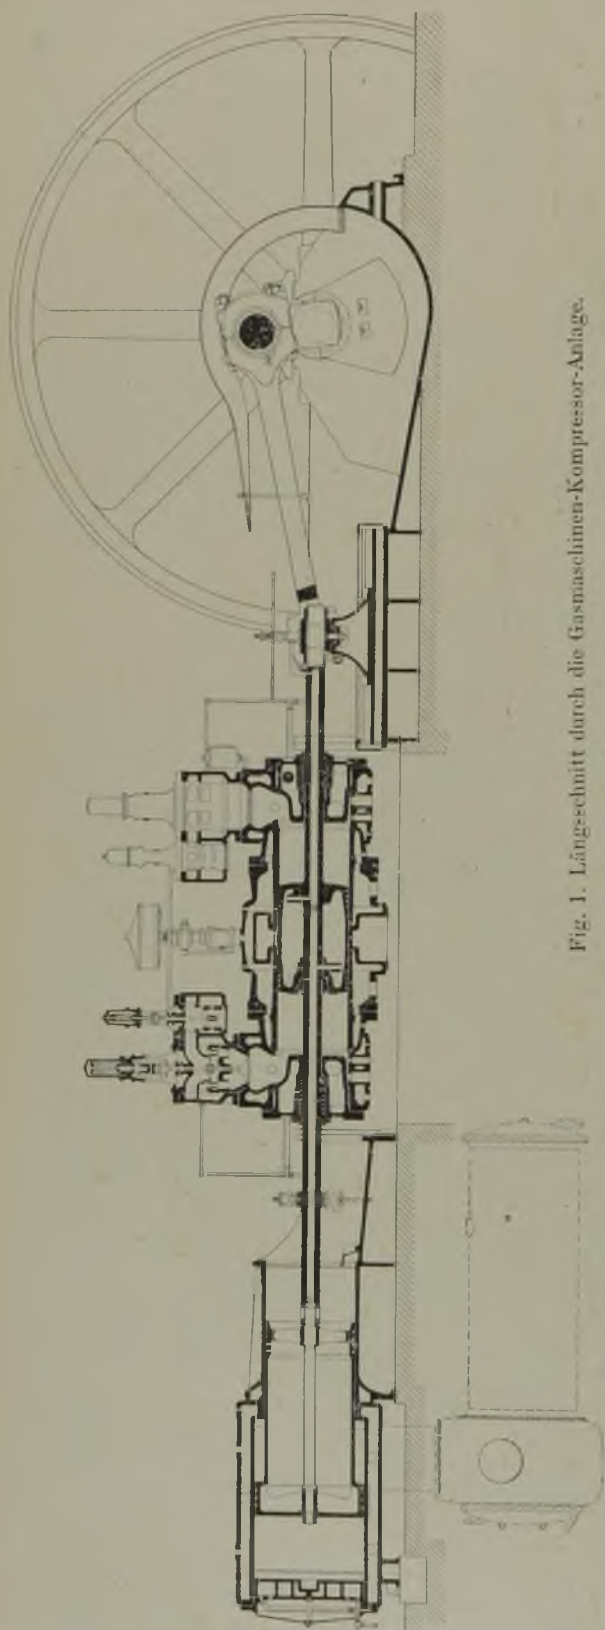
Längsschnitt durch die Gasmaschinen-Kompressor-Anlage.
